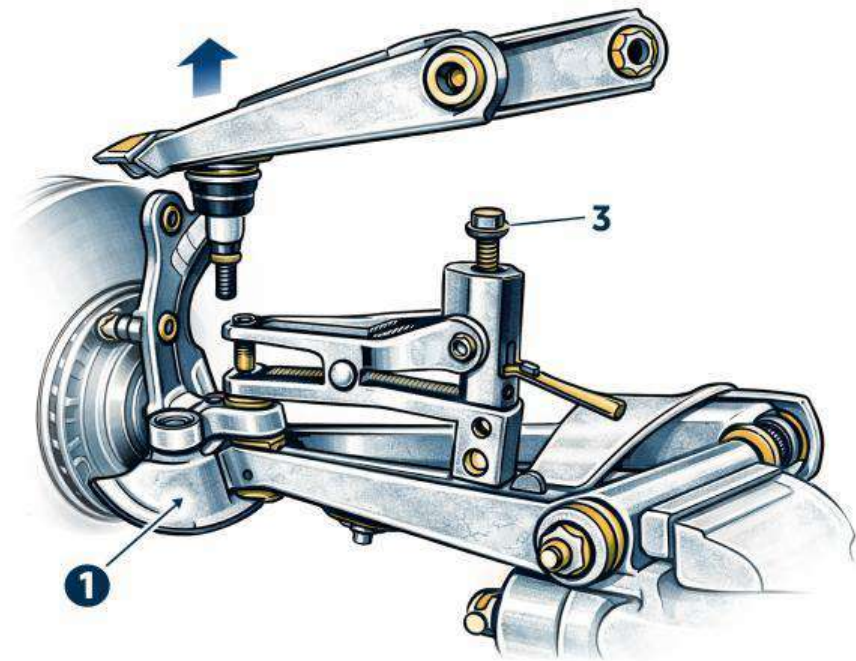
Від'єднання верхнього важеля: 1 - обертовий кулак; 2 - палець шарового шарніра; 3 - пристрій; 4 - болт
